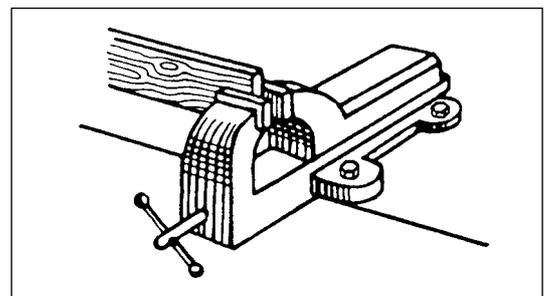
Les serre-joints peuvent aussi maintenir des pièces travaillées de différentes formes et dimensions et libérer les mains
